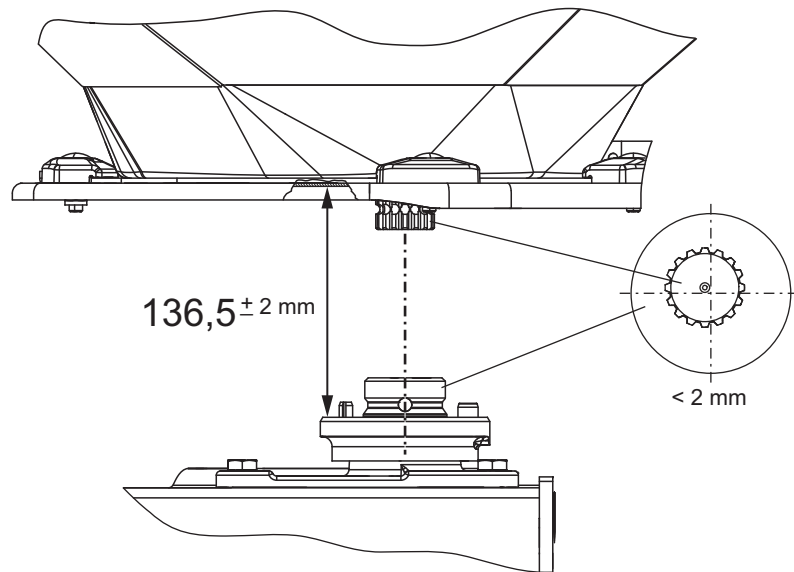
Проверка положения втулки разбрасывающего диска
